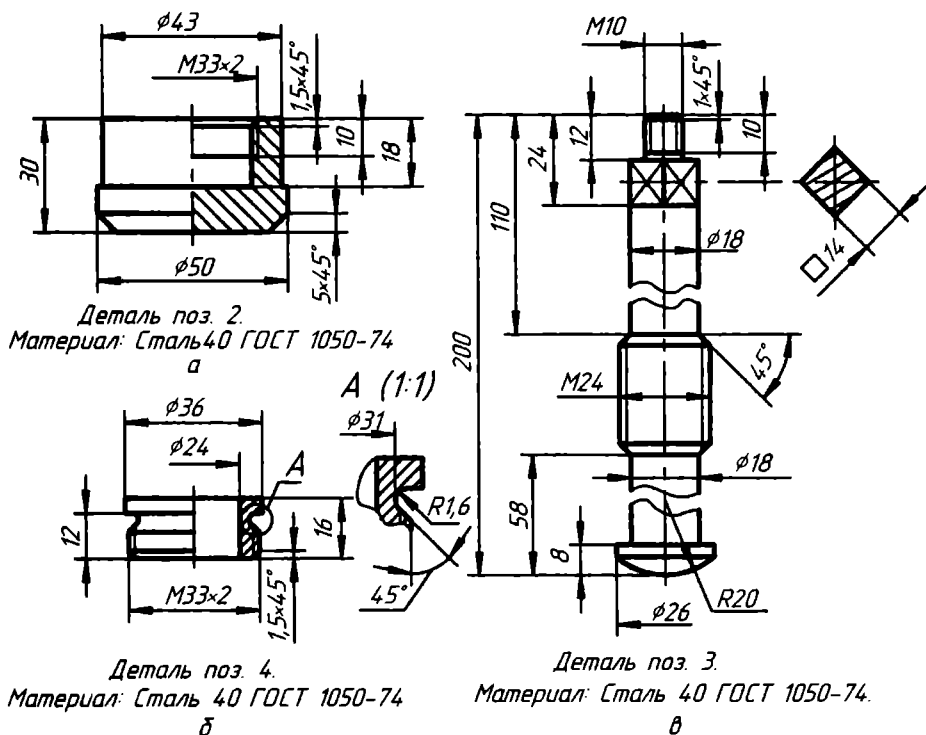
Чертежи: а — клапана; б — втулки; в — шпинделя
